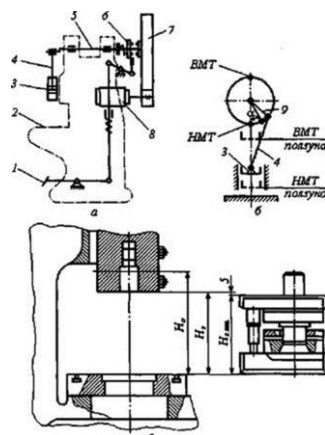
Кривошипный прес: а - схема пристрою преса, б - схема роботи кривошипно-шатунного механізму, в - схема установки штампа на стіл преса; 1 - педаль включення, 2 - стіл преса, 3 - повзун, 4 - шатун, 5 - кривошипний вал, 6 - муфта, 7 - махове колесо, 8 - електродвигун, 9 - кривошип
